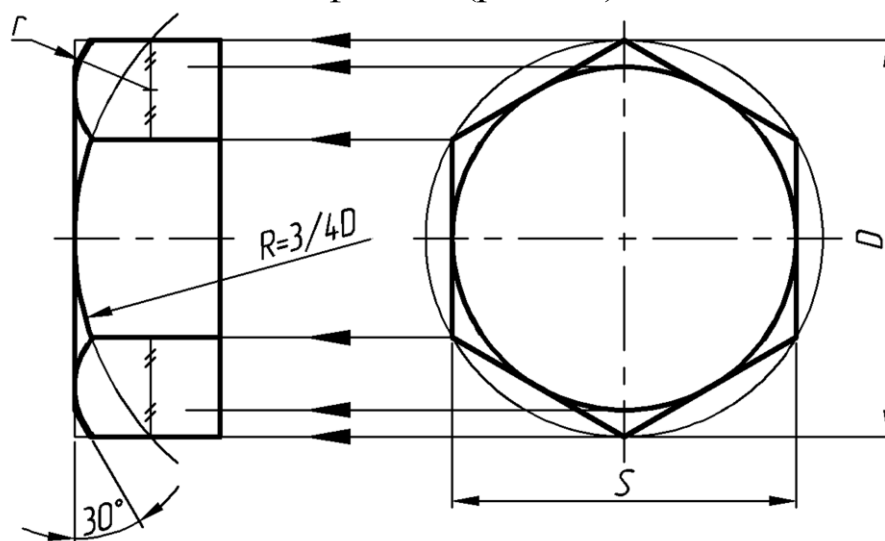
Шестигранная головка болта и гайка с конической фаской
